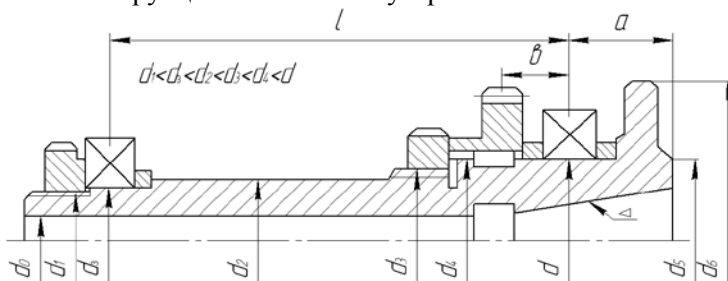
Конструктивная схема шпиндельного узла и основные конструктивные размеры
